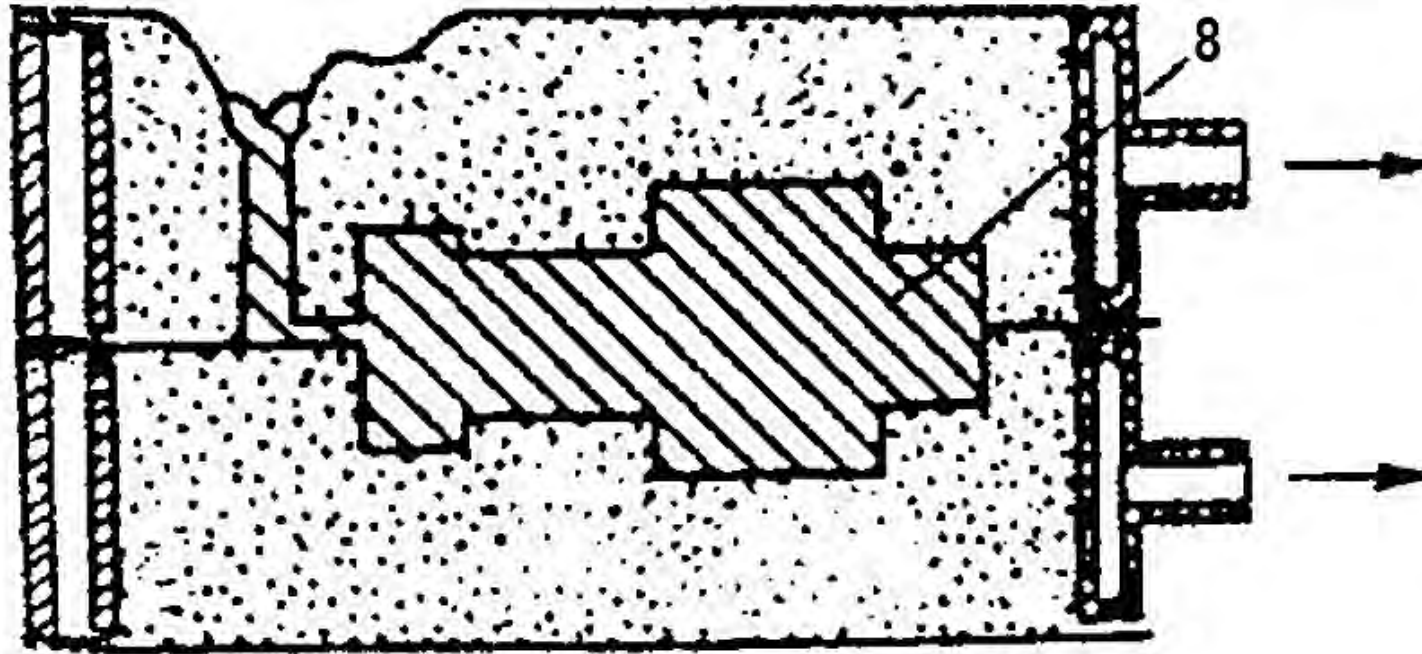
Установка стержня в нижнюю полуформу и сборка формы: 8 – стержень
